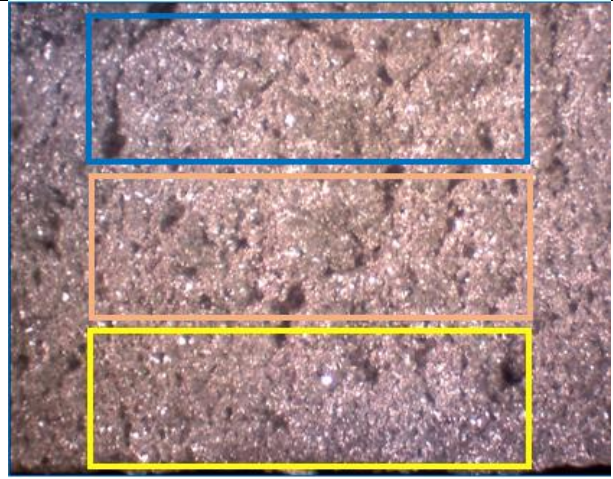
Fractura de la sección 2 de la probeta del ensayo de impacto.
